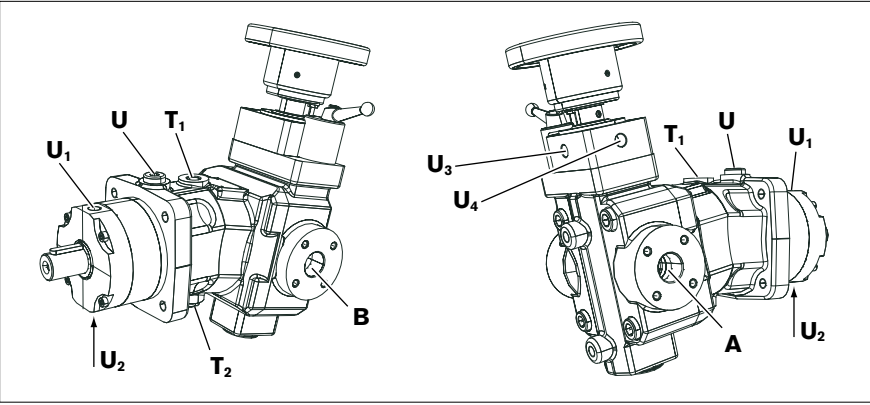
Anschlussübersicht A7VK, geschlossene Bauart
